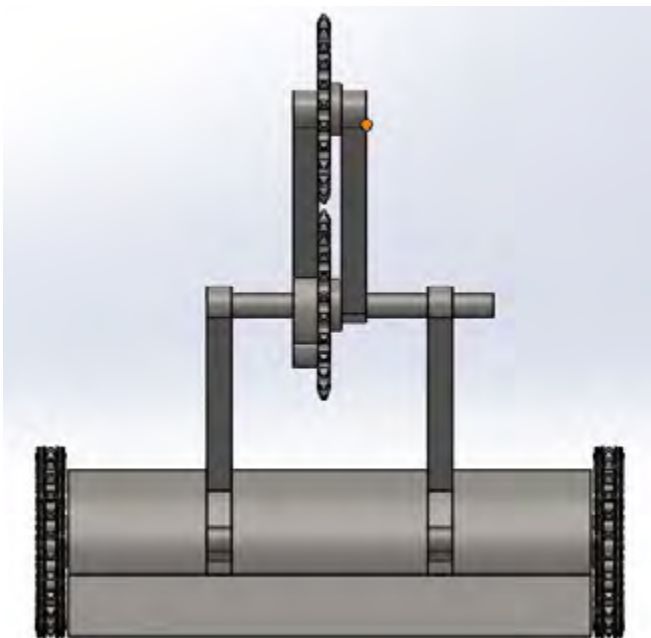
Vista frontal del sistema mecánico en Solidworks.
